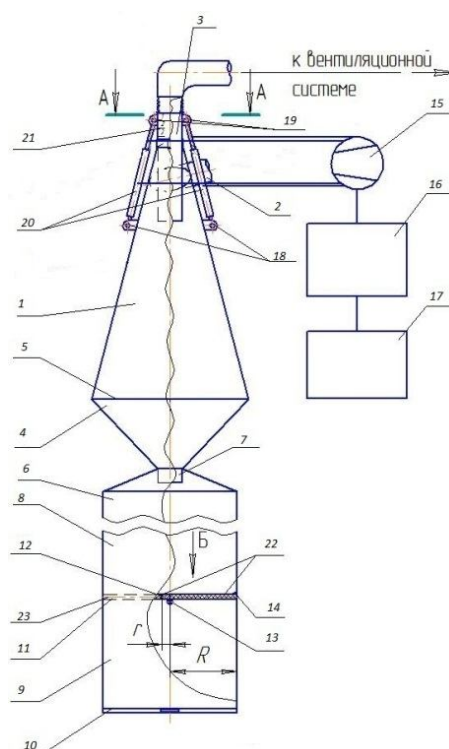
Пылеулавливатель: 1- верхний конус циклона, 2-входной патрубков, 3- выхлопной патрубков, 4-нижний конус циклона, 5 - основания конусов, 6 - пылесборник, 7 - патрубков, 8 - верхний отсек пылесборника, 9 - нижний отсек пылесборника, 10 – задвижка, 11– перегородка, 12 – полукруглые люки, 13 - противовесы, 14 – ось, относительно которой вращается перегородка, 15-нагнетательное устройство, 16- блок управления, 17- источник питания, 18 - кольцевой упор, 19 - проушины, 20 - основания пневмоцилиндров, 21 - выдвижные штоки пневмоцилиндров, 22 – шкала с делениями, 23 – кольцевой упор.
